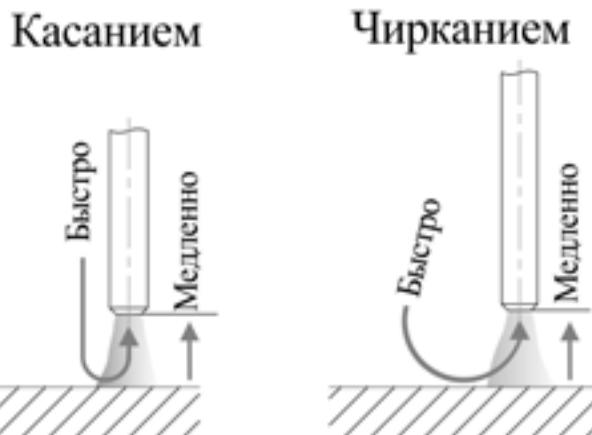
Способы зажигания сварочной дуги.
